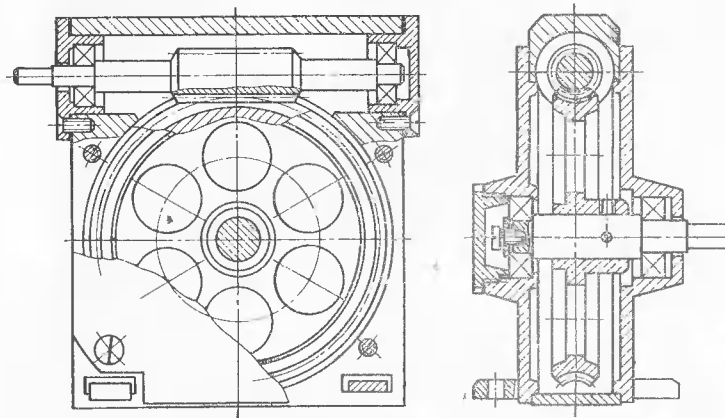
Конструкция червячного редуктора с корпусом, выполненным механической обработкой
